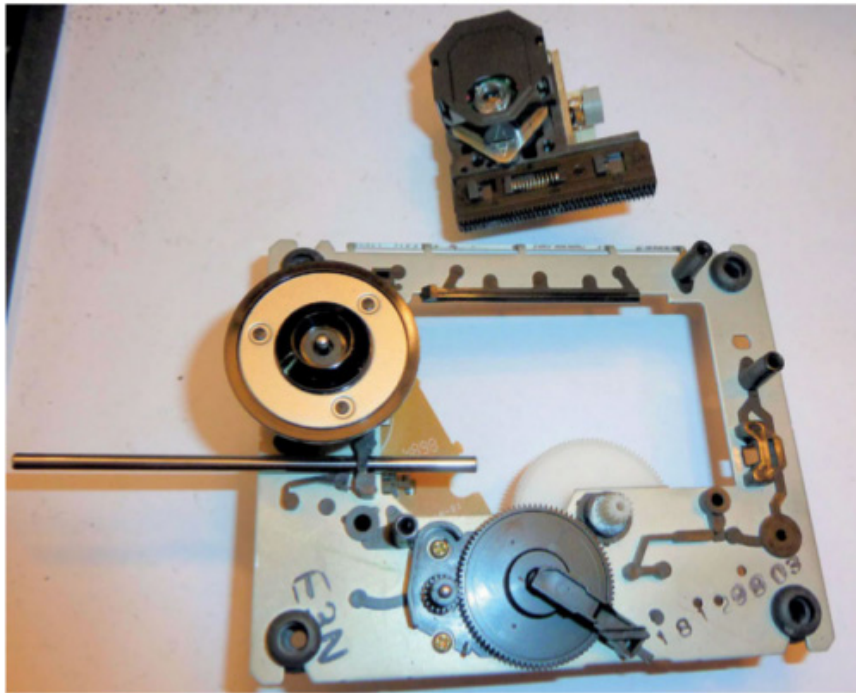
Bloc optique démonté après libération de la glissière unique
